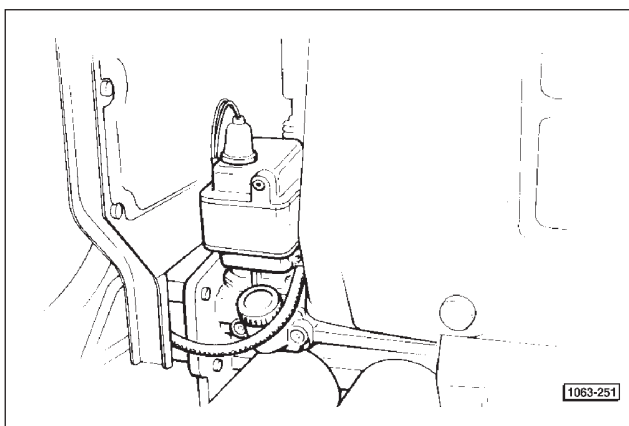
Seulement pour tracteurs équipés d'un régulateur électronique : monter l'actionneur du régulateur ;
